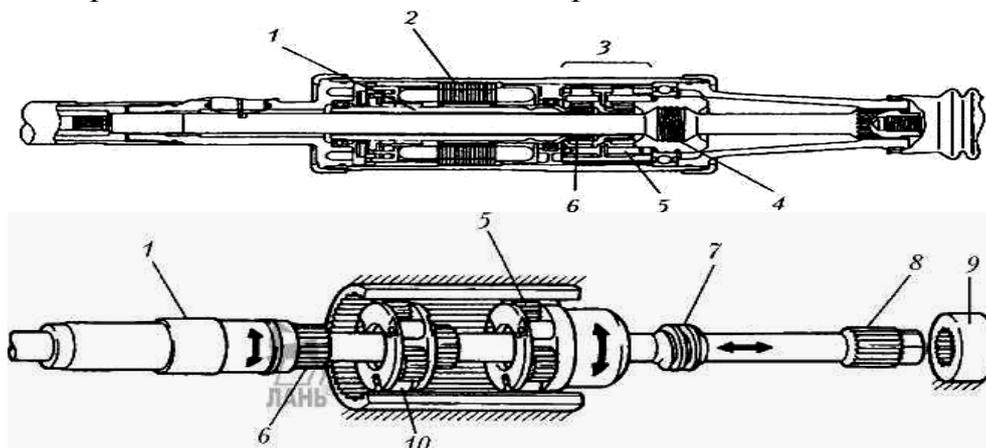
Электромеханический исполнительный механизм поворота задней оси: 1 — пустотелый вал ротора; 2 — статор; 3 — планетарная коробка передач; 4 — гайка шпинделя; 5 — сателлит; 6 — солнечная шестерня; 7 — шпиндель (винт); 8 — шлицевая часть вала шпинделя; 9 — предохранитель от прокручивания шпинделя; 10 — водило планетарной передачи.
